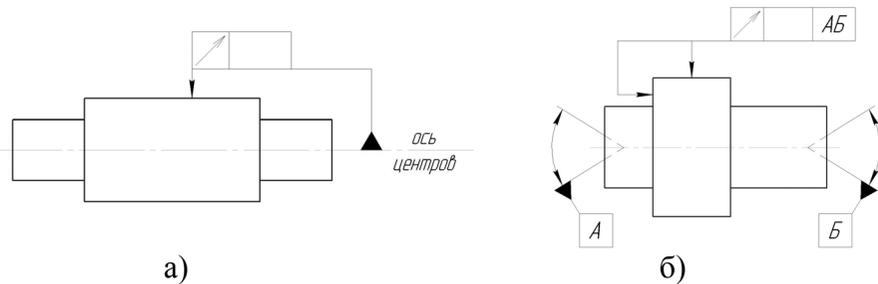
Допускаемые стандартом обозначения базовой оси центров отверстий
